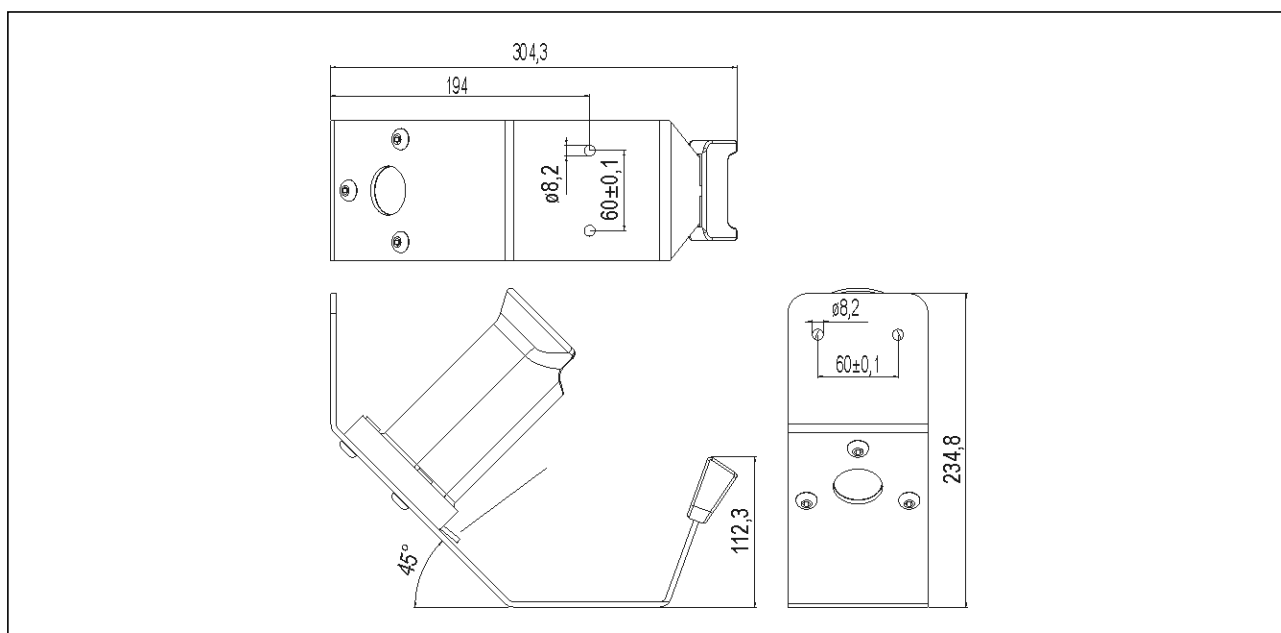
Dimensioni supporto dell'utensile (mm)
